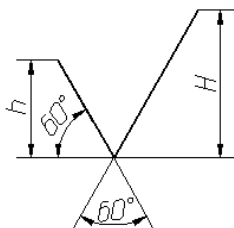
Обозначение шероховатости поверхности без указания способа обработки
